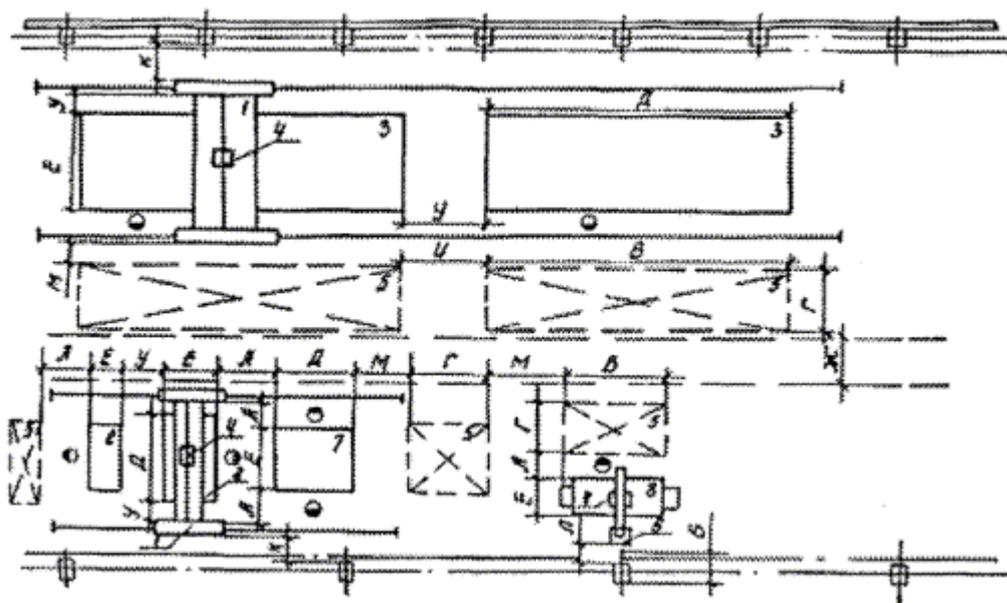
Размещение установок автоматической сварки и резки с поворотными колоннами и самоходными порталами:
